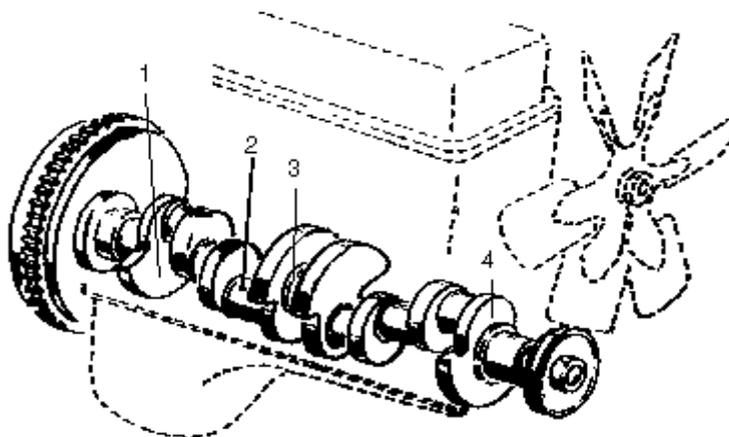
Representação de uma cambota de um motor de quatro cilindros.
